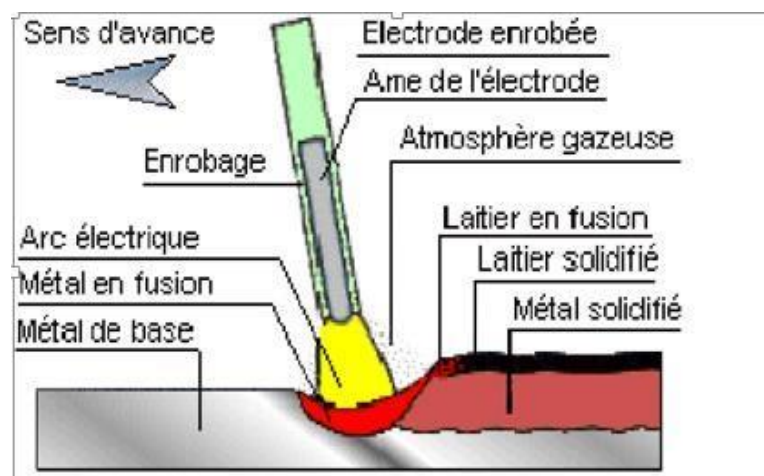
Principe de soudage à l'arc avec électrodes enrobées [10]
